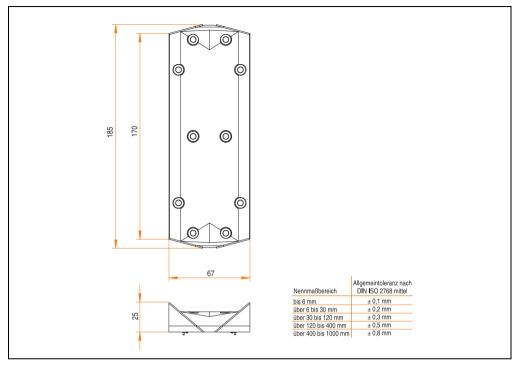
Abmessungen Extension Connector 5AC800.CON1-00
